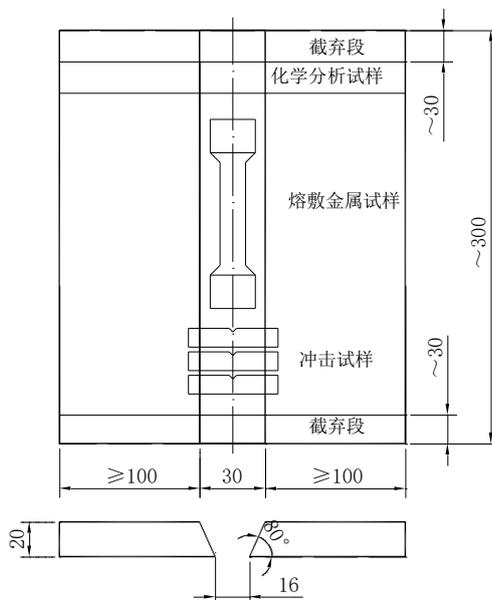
熔敷金属对接焊试件的取样位置
